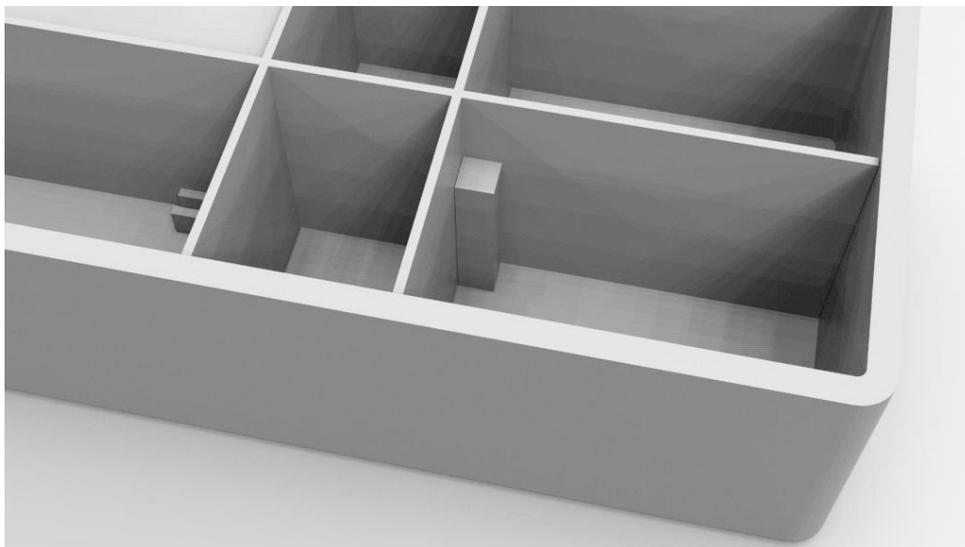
Detalle para acoplar el perfil de techo Pick-Up
